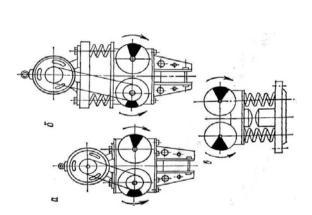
Рис. I. Схемы вибропогружателей: a-c жестким креплением двигателя; 6-c подрессорной пригрузкой; s-вибромолот
